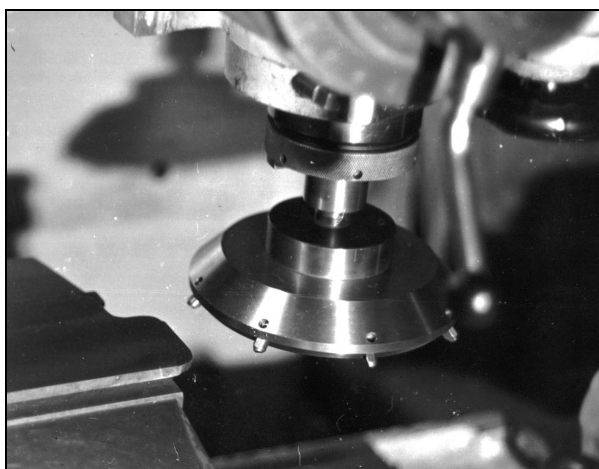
Пример нежесткой установки торцевой фрезы на оправке в шпинделе станка
